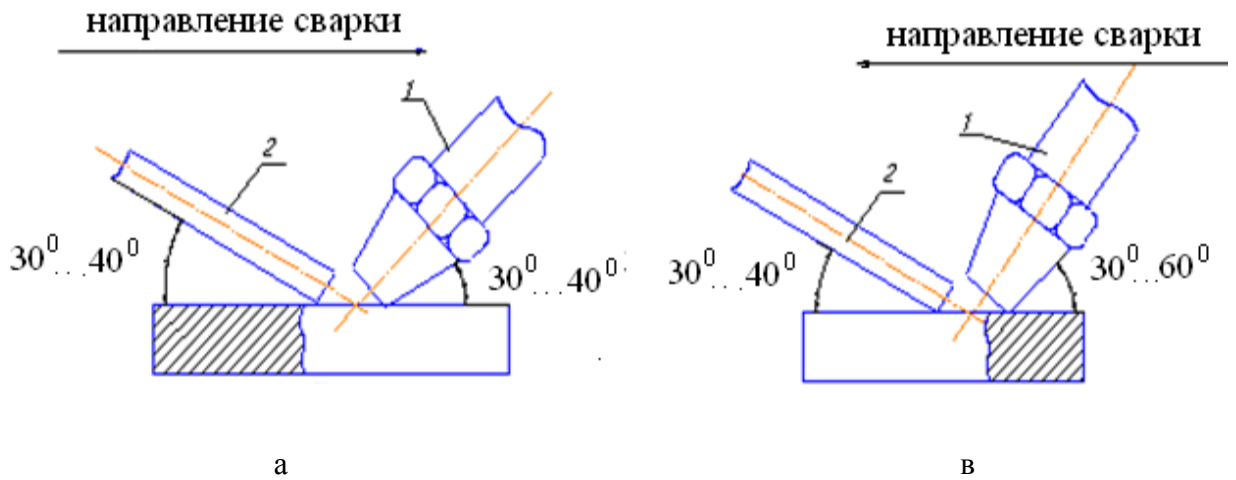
Способы газовой сварки металла и углы наклона горелки и присадочного прутка:
